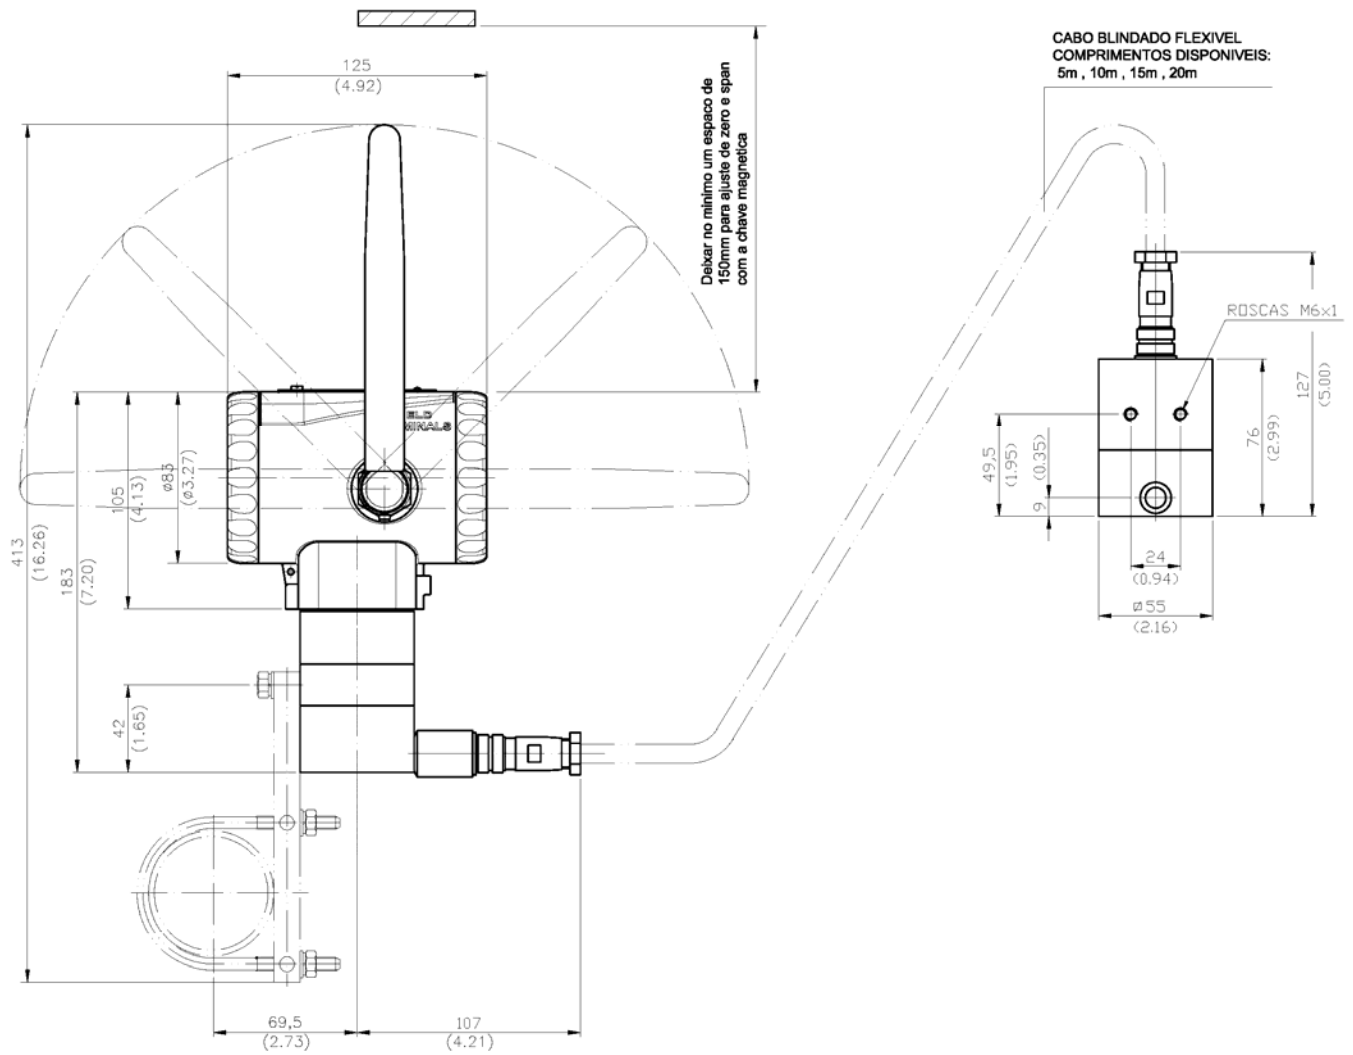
6 – Desenho Dimensional de Montagem do TP400 WirelessHART™ na vertical com Sensor Remoto
